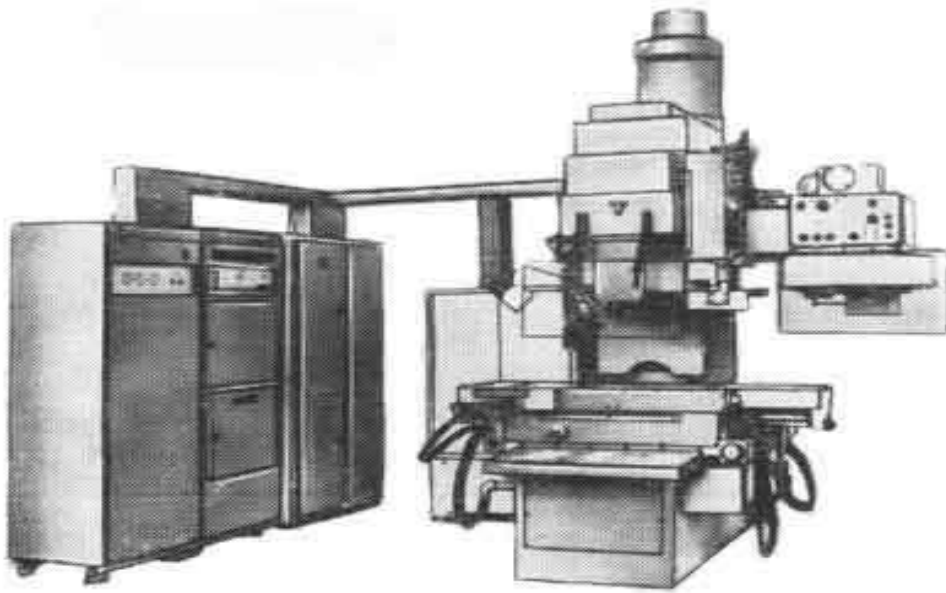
Станок вертикально-фрезерный 6520МФЗ
